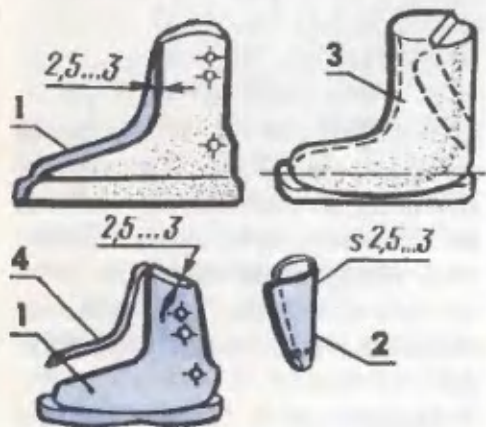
Детали ботинка и «болван»: 1 — заготовка передней части ботинка; 2 — заготовка задника; 3 — модель ботинка — «болван»; 4 — лента для склеивания половинок передней части ботинка (стеклоткань).
